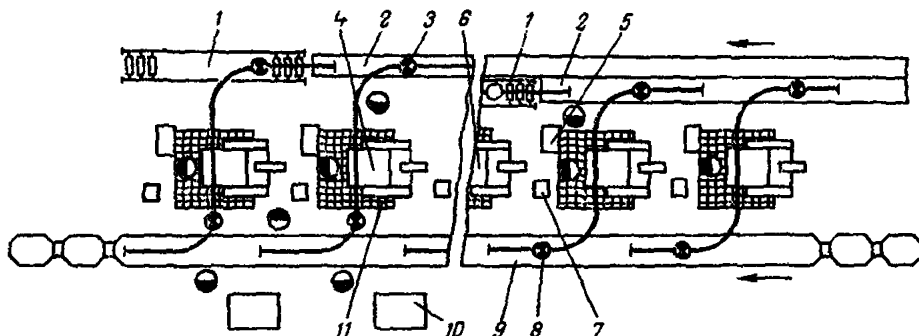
Схема планировки рабочего места формовщика средних отливок при групповом расположении формовочных машин:
